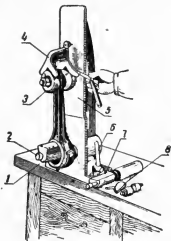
Приспособление для проверки относительного расположения верхней и нижней головок шатуна:
